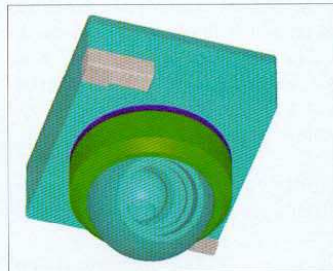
Kompaktes und schlüssiges Konstruktionsprinzip: Im Kugelschwenkkopf sind 30 Prozent weniger Bauteile integriert als in herkömmlichen Rotations-Schwenkköpfen
